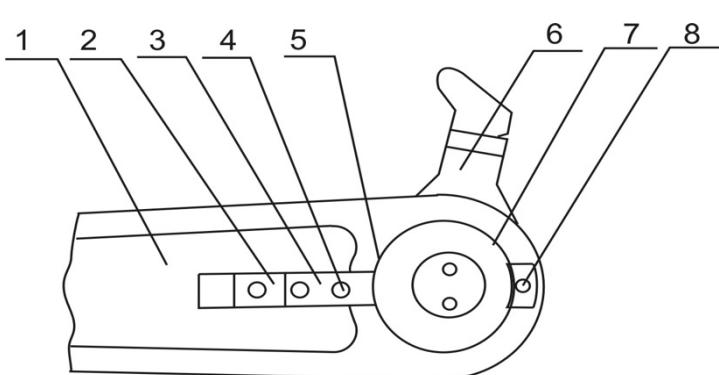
Установочный механизм эксцентриковой зубчатой передачи
